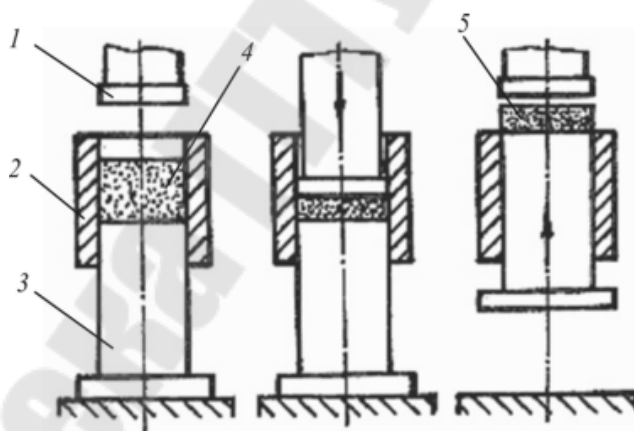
Схема прессования: 1 - пуансон; 2 - матрица; 3 - выталкиватель; 4 - порошок; 5 - отформованная заготовка
